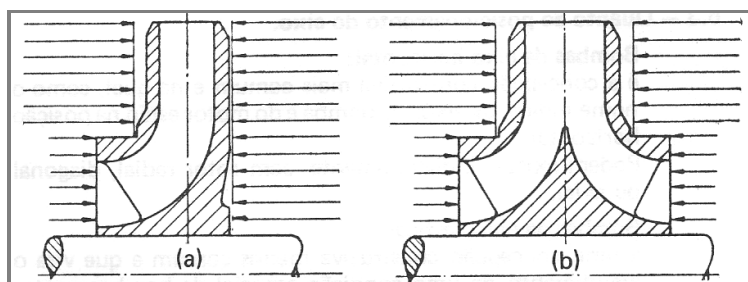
Rotor de simples sucção (a) e rotor de dupla sucção (b).
